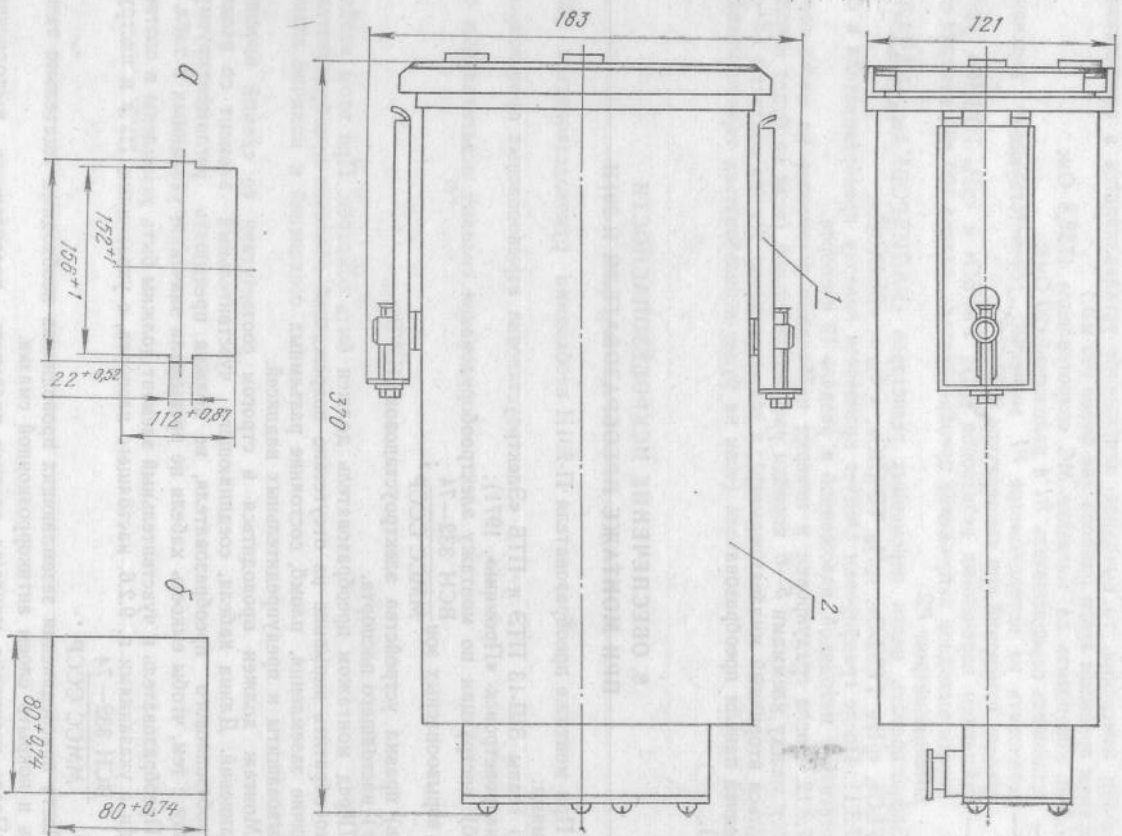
Габаритные и присоединительные размеры преобразователя и ТКР-3:
